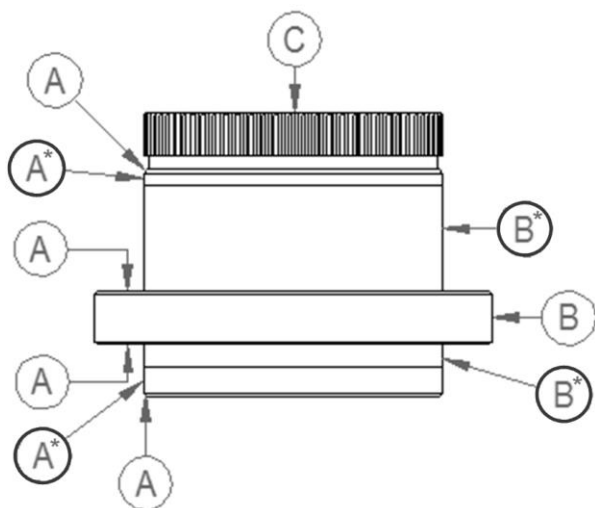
Шлицевая ведущая втулка - важные поверхности
